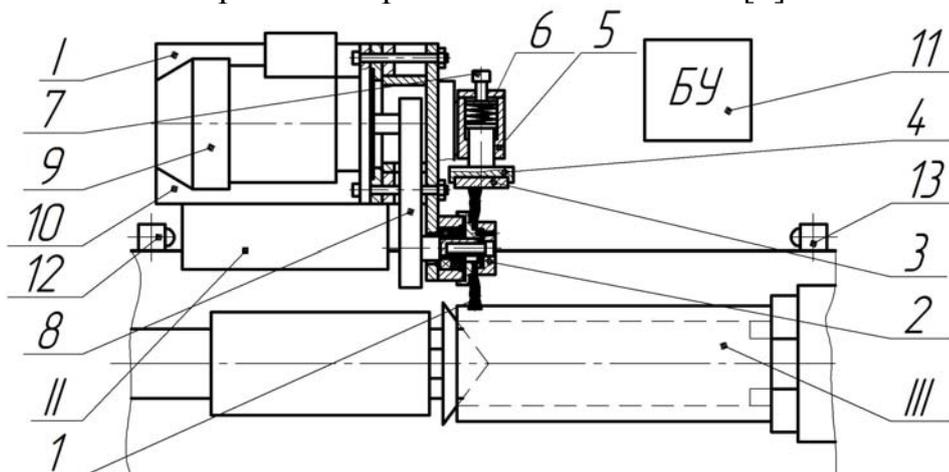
Схема механизированной установки и устройства для ПГИ цилиндрических наружных поверхностей
